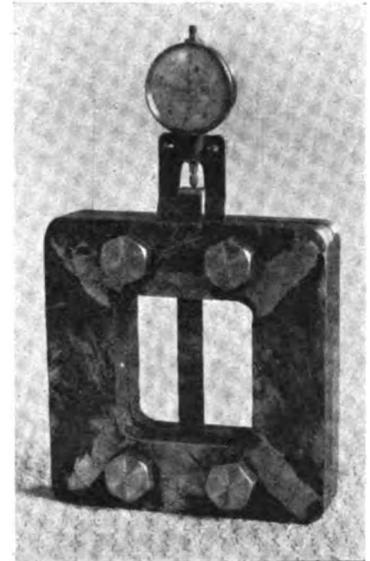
Vorrichtung zur Bestimmung der linearen Schweißverformung senkrecht zur Schweißnaht. Der Schweißstab ist unten fest eingespannt, oben besteht etwa 0,1 mm Spiel.
